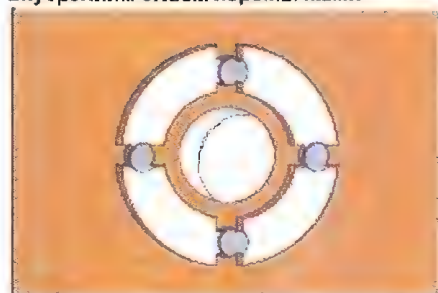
Фрезерование рядом с металлизированным отверстием для разрушения перемычек
